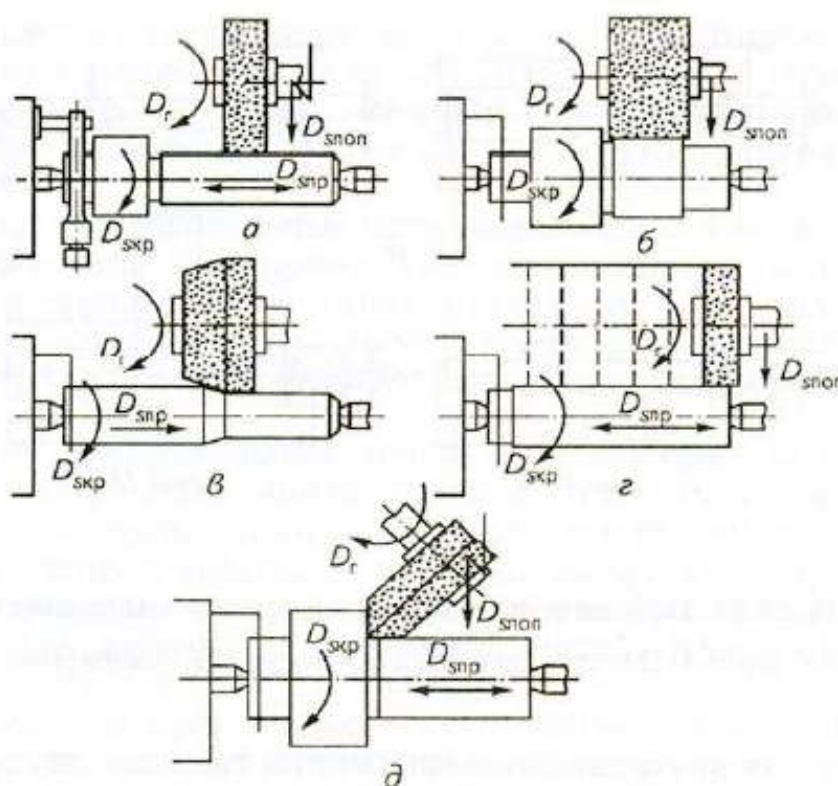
Схемы обработки заготовок на круглошлифовальных станках
